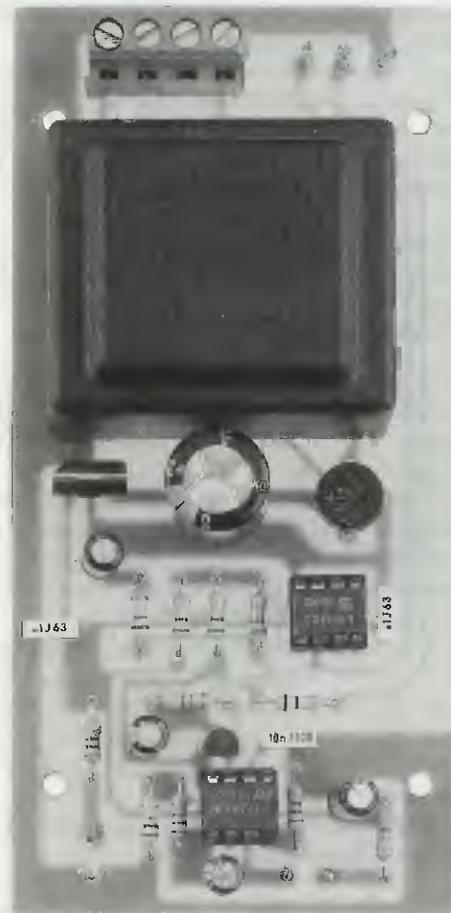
Foto del circuito stampato con sopra già fissati tutti i componenti.
